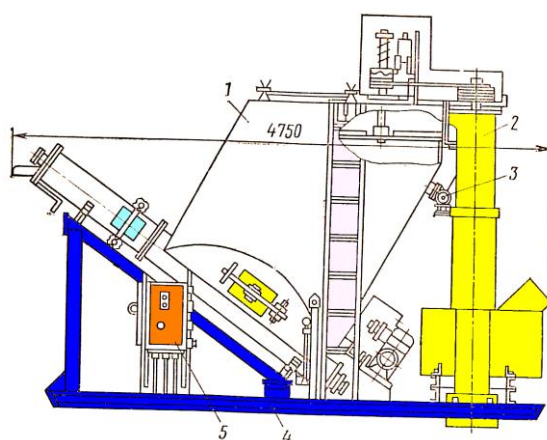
Кормоприготовительный агрегат-запарник ЗПК-4:
